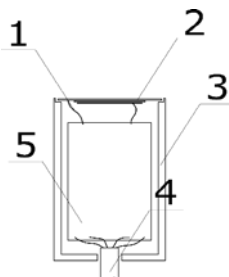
Конструкция гидрофона. 1 — соединительные провода; 2 — пьезоэлемент; 3 — алюминиевый корпус; 4 — многожильный кабель; 5 — усилитель сигнала.
